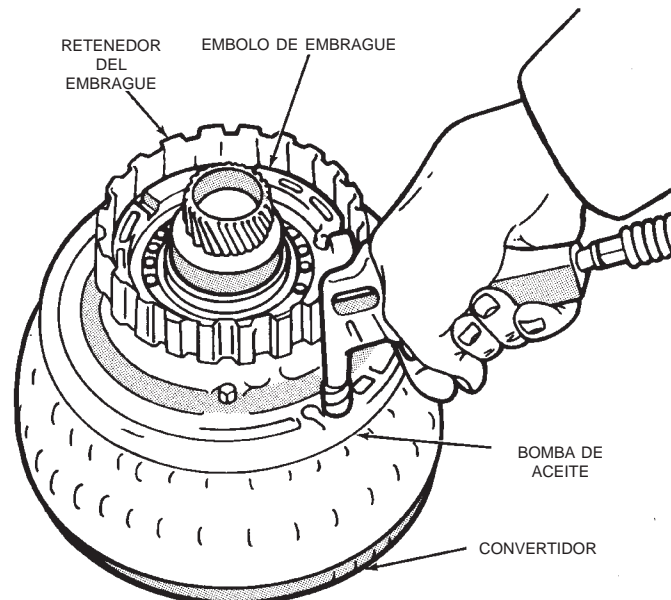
Desmontaje del émbolo del embrague de sobremarcha
